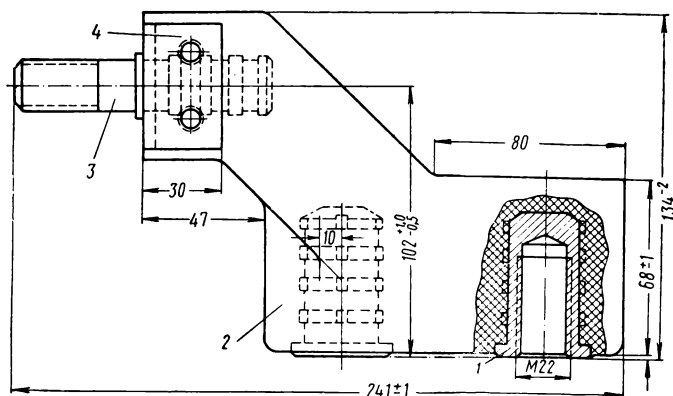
Кронштейн щеткодержателя тягового двигателя ДК-103Г из стеклопластика АГ-4В:
